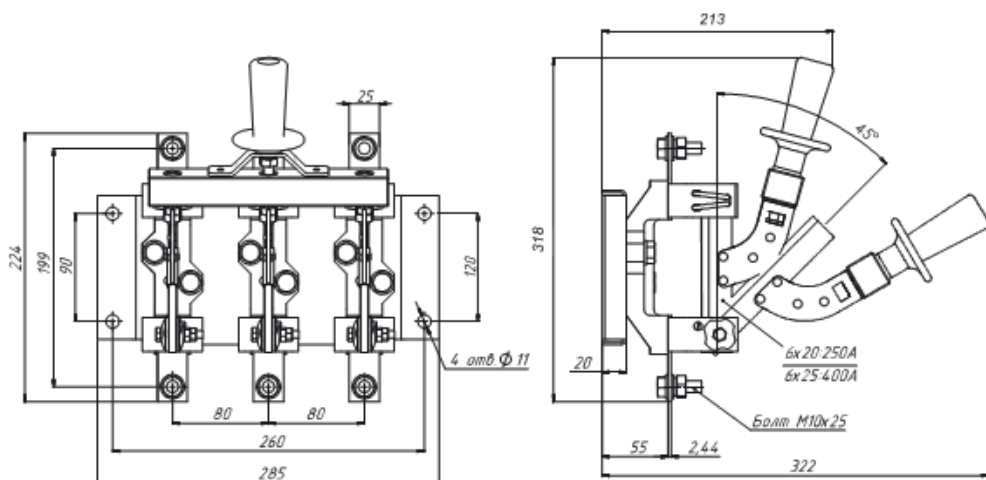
Разъединитель РЕ19–35(37)–31190–00 УХЛЗ с центральным рычагом для управления штангой
